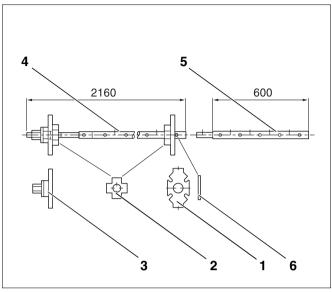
Kesselpresswerkzeug Größe 2.2 (Maße in mm)
